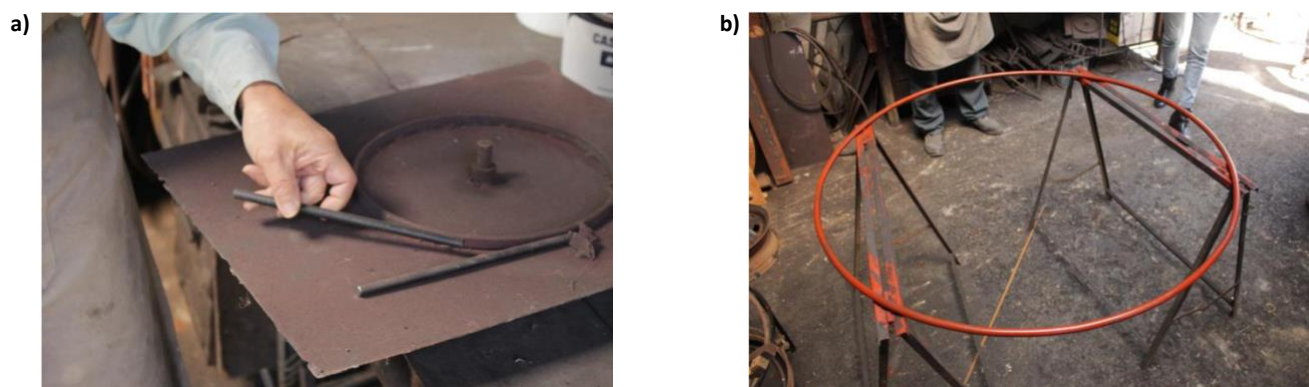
Preparo das ferragens: a) detalhe do molde para dar forma à barra de ferro, b) aro com zarcão
